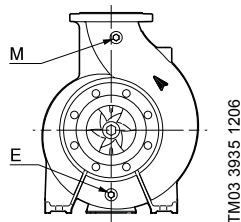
Сливная пробка и пробка для выпуска воздуха
